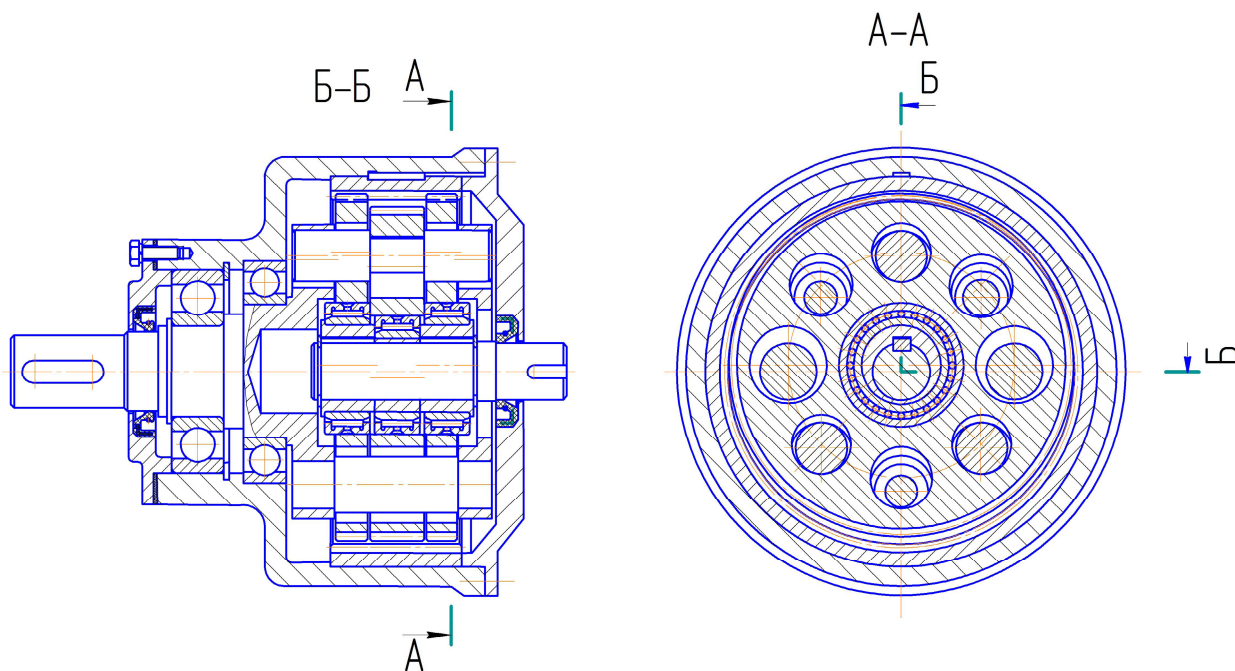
Планетарная передача с малой разницей чисел зубьев колес и роликовым механизмом снятия движения с сателлитов
